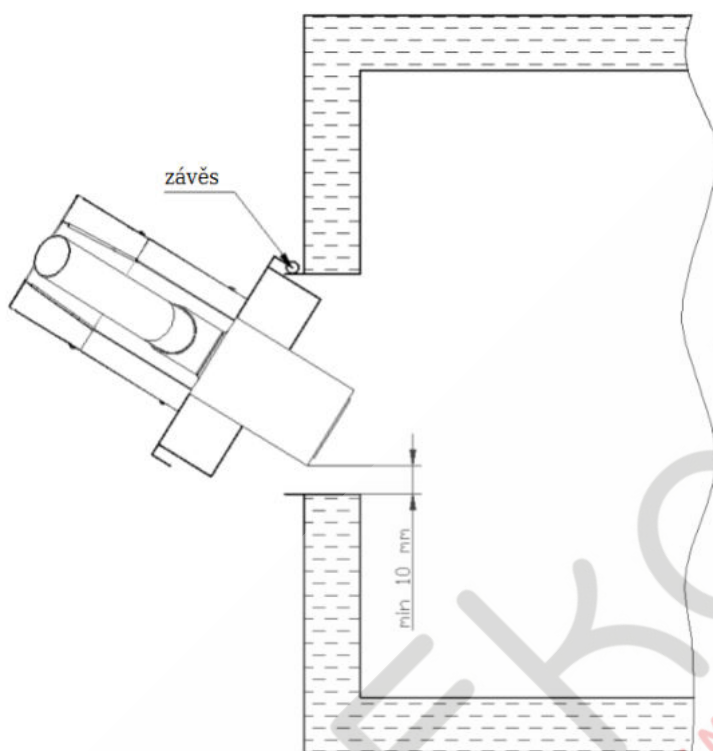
Schéma vytváření montážních otvorů pro hořák s izolačním pláštěm a montážní deskou pro hořáky: 4-16 kW, 5-20 kW, 6-26 kW, 8-36 kW.
